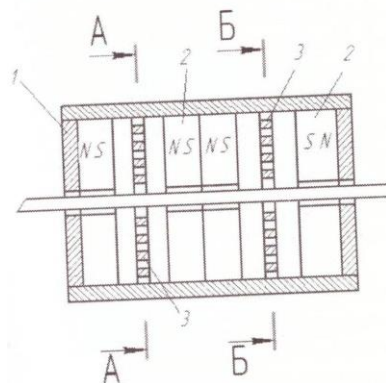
Композитный модернизированный двухспиральный двигатель: 1 - корпус; 2 - постоянные магниты; 3- композитная спиральная электропроводящая пружина.
